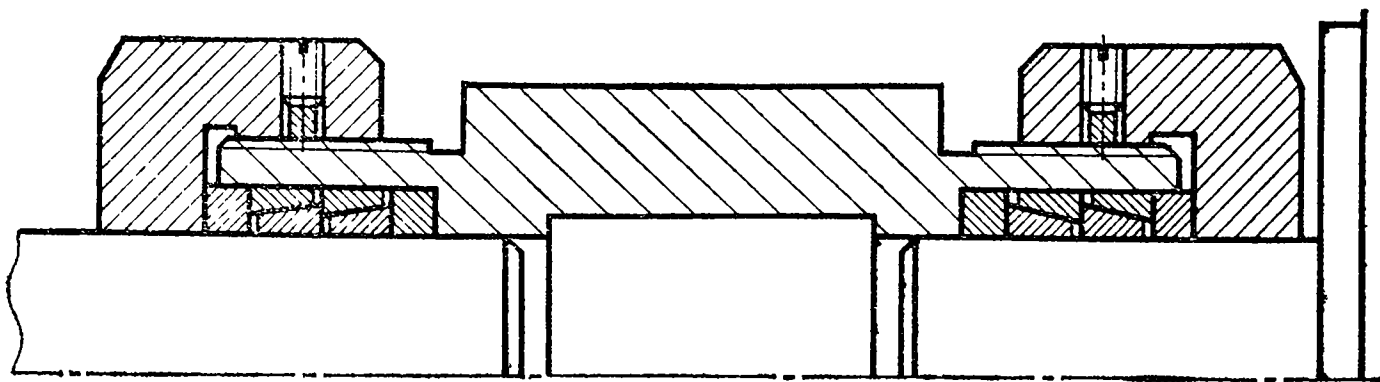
Жесткая муфта для связи вала двигателя и ходового винта
